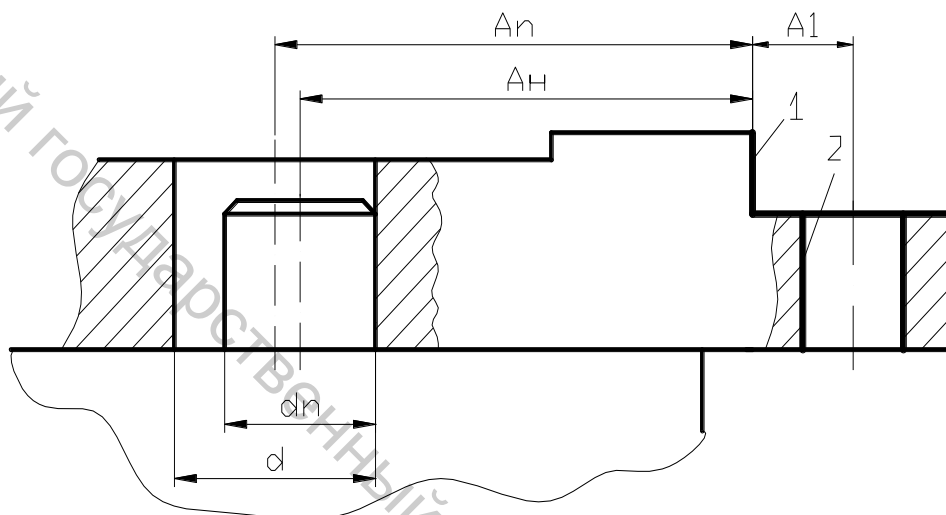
Установка заготовки по отверстию на цилиндрический палец
